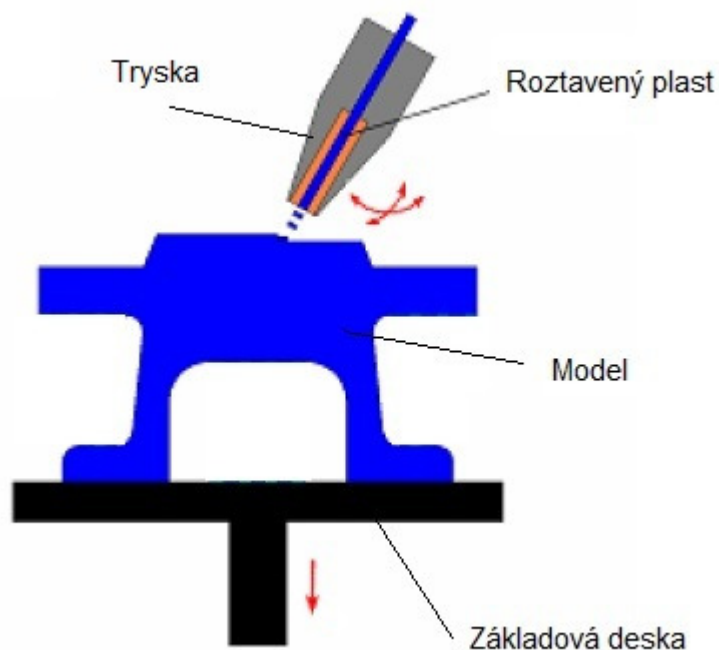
Schéma technologie Model Maker 3D petting [6]
